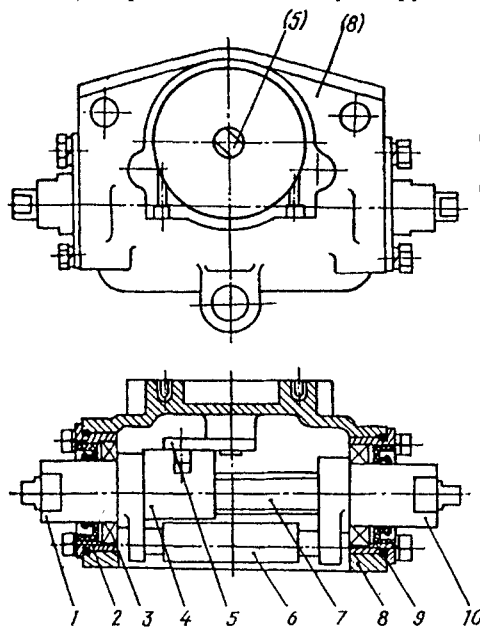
Смеситель сигналов датчиков (МТЗ-100 и МТЗ-102): 1 – позиционный рычаг; 2 – манжета; 3 – подшипник; 4 – суммирующий рычаг; 5 – рычаг; 6 – коромысло; 7 – валик; 8 – корпус; 9 – крышка; 10 – силовой рычаг
